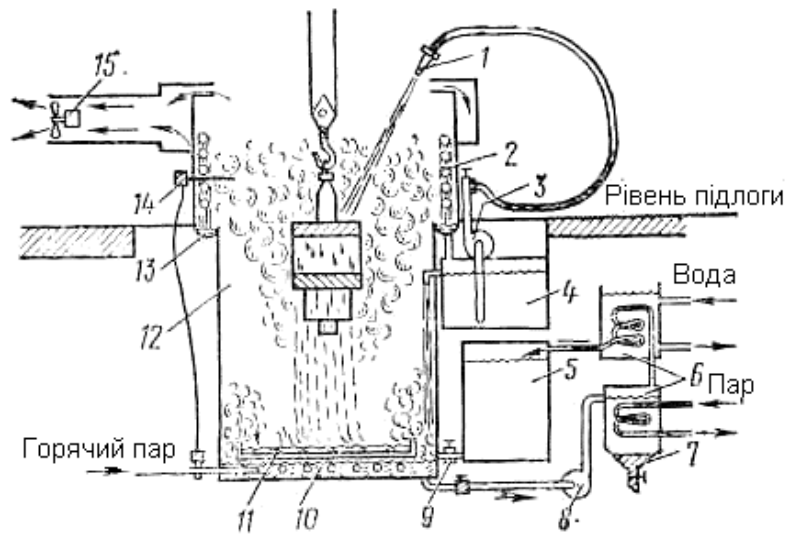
Схема пристрою для очищення деталей парами розчинника:
